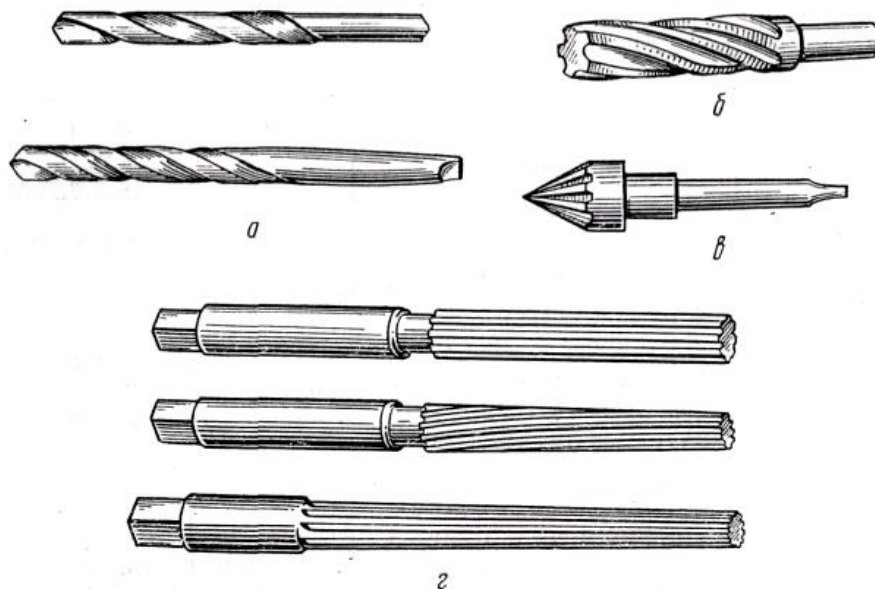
Інструменти для свердління і розгортання отворів:
